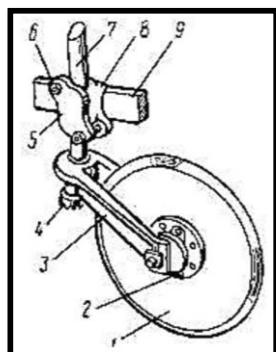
Нож дисковый: 1 – диск; 2 – фланец; 3 – вилка; 4 – шайба корончатая; 5 – накладка державки; 6 – болт; 7 – стойка; 8 – державка; 9 – продольный брус рамы.
